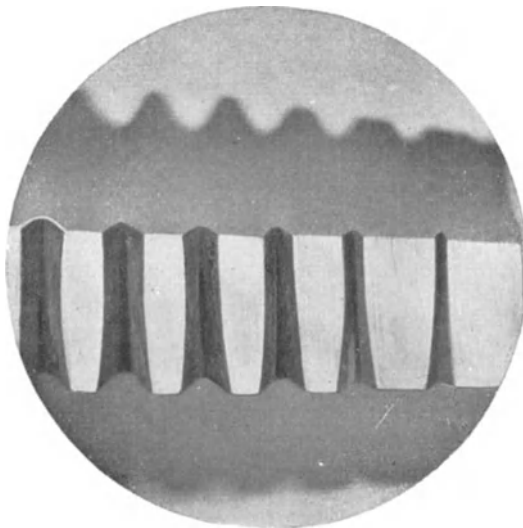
Im Anschnitt hinterschliffener Gewindebohrer.
